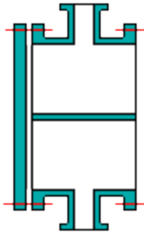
Cabezal frontal de canal y cabeza removible (tipo A)
